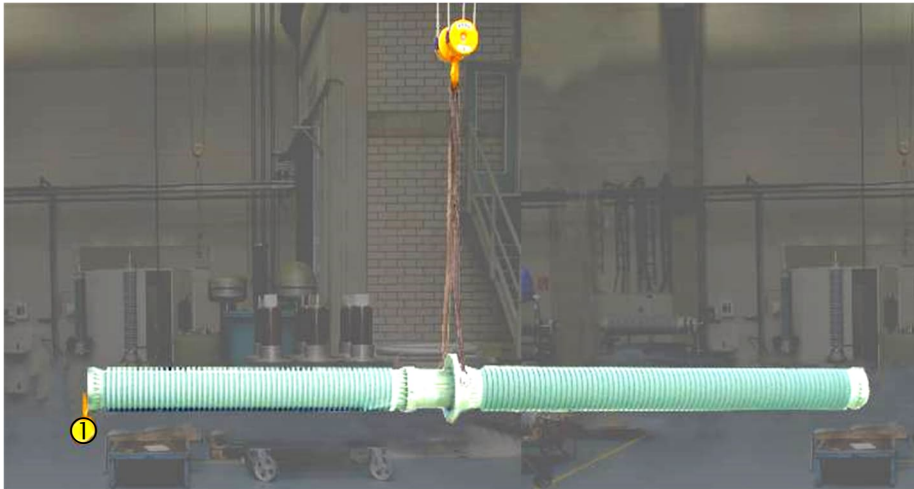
Anheben einer Wanddurchführung mit Gegengewicht
